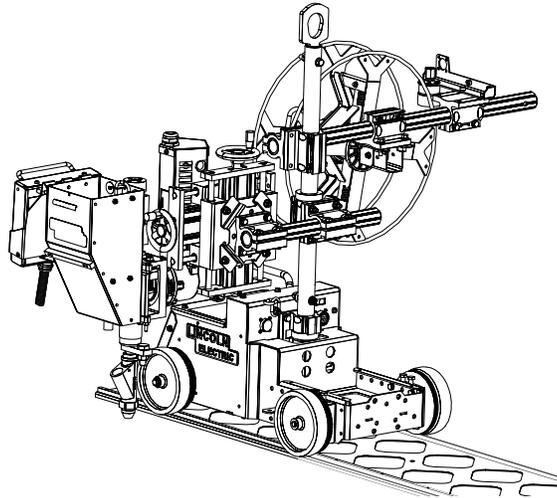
VISTA POSTERIOR DE LA SOLDADURA DE CARRIL
